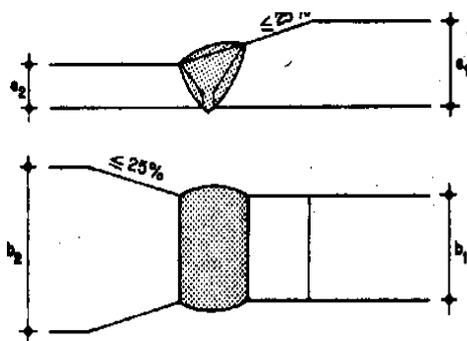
Soldadura A-TOPE, distintas secciones
